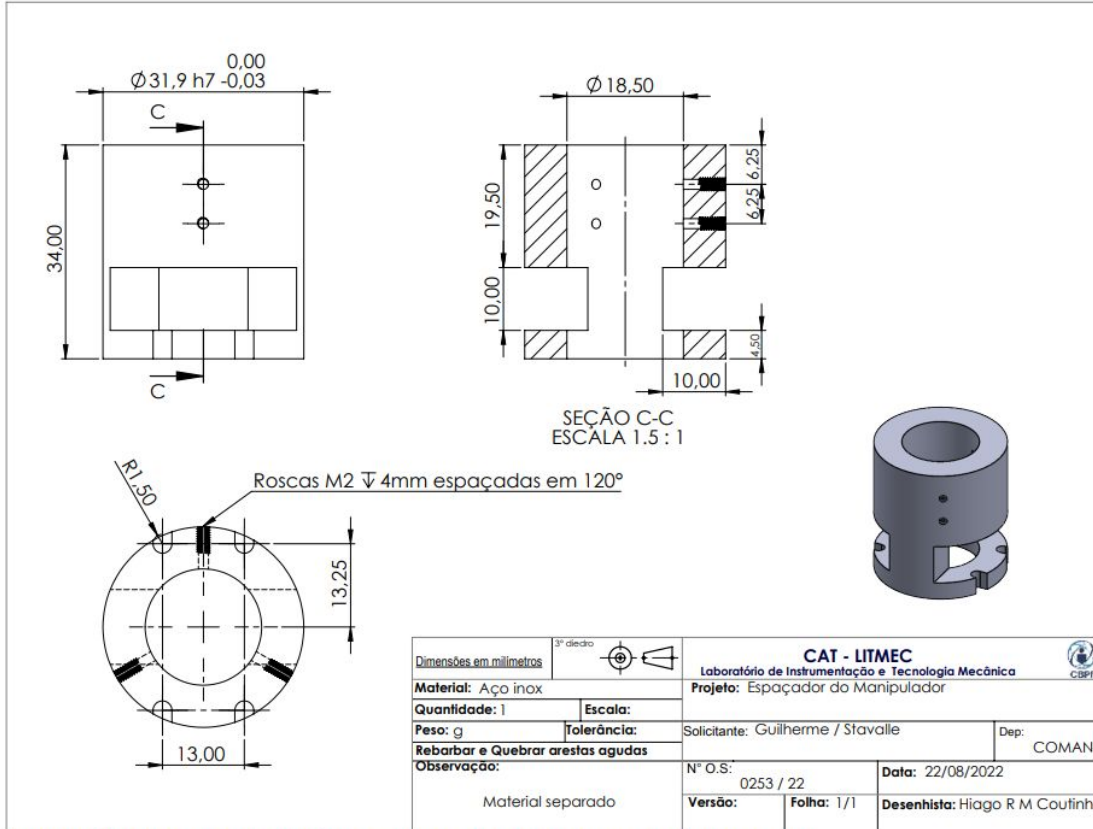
Desenho técnico de suporte para sulfetos. Fonte: LITMEC, 2022.
